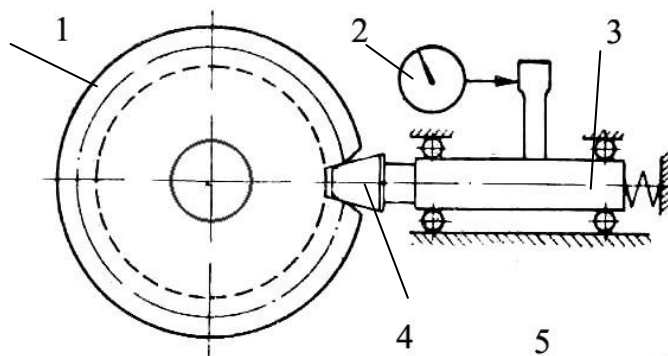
Схема контроля радиального биения венца зубчатого колеса
